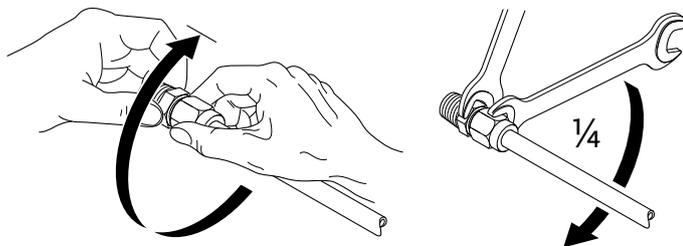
Ruotare ulteriormente il raccordo a compressione di 1/4 di giro
